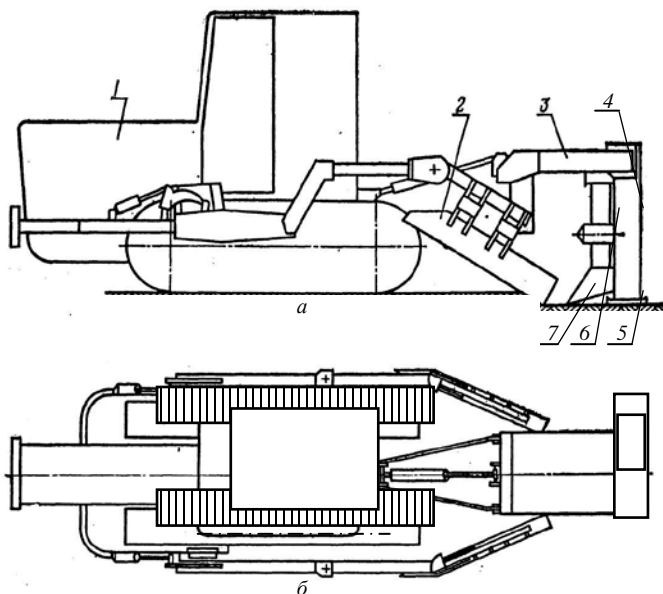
Схема отвально-фрезерного каналочистителя: *a* – вид сбоку; *б* – вид сверху; 1 – трактор; 2 – отвалы; 3 – рама; 4 – цепной редуктор; 5 – лыжа; 6 – фреза; 7 – лемех
